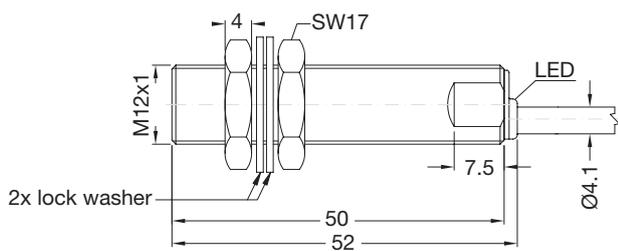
Lange Ausführung, bündiger Einbau, Kabel
